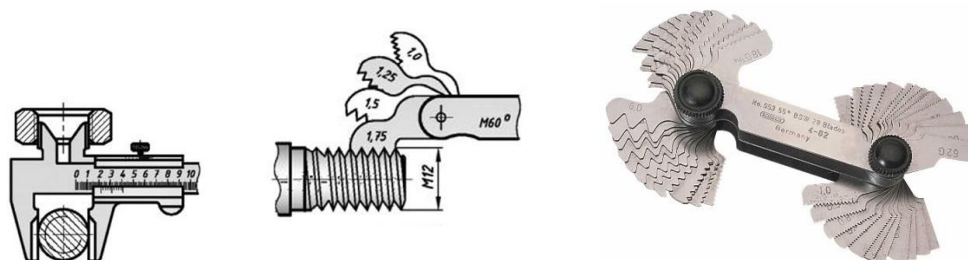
Измерение диаметра резьбы штангенциркулем и шага резьбы резьбомером
